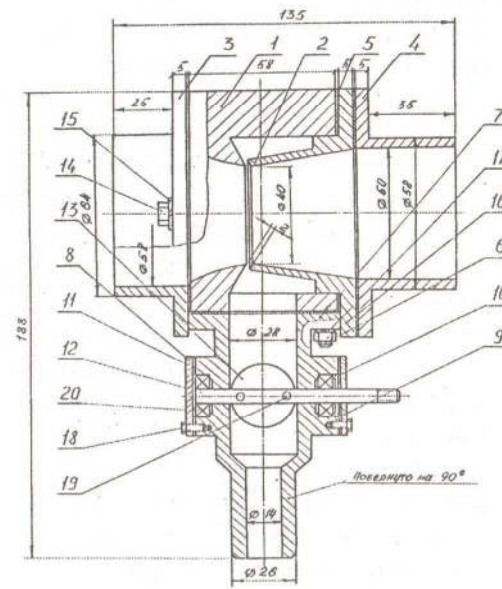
Газовоздушный смеситель-дозатор для подачи природного газа дизеля 4Ч 10,5/12,0: 1 - корпус; 2 - диффузор; 3 - патрубок воздушный; 4 - патрубок соединительный; 5 - прокладка; 6 - шпилька; 7 - корпус дозатора; 8 - крышка глухая; 9 - крышка; 10 - шайба уплотнительная; 11 - прокладка; 12 - ось заслонки; 13 - заслонка газовая; 14 - болт соединительный; 15 - шайба; 16 - гайка; 17 - шайба; 18 - болт; 19 - винт; 20 - подшипник
